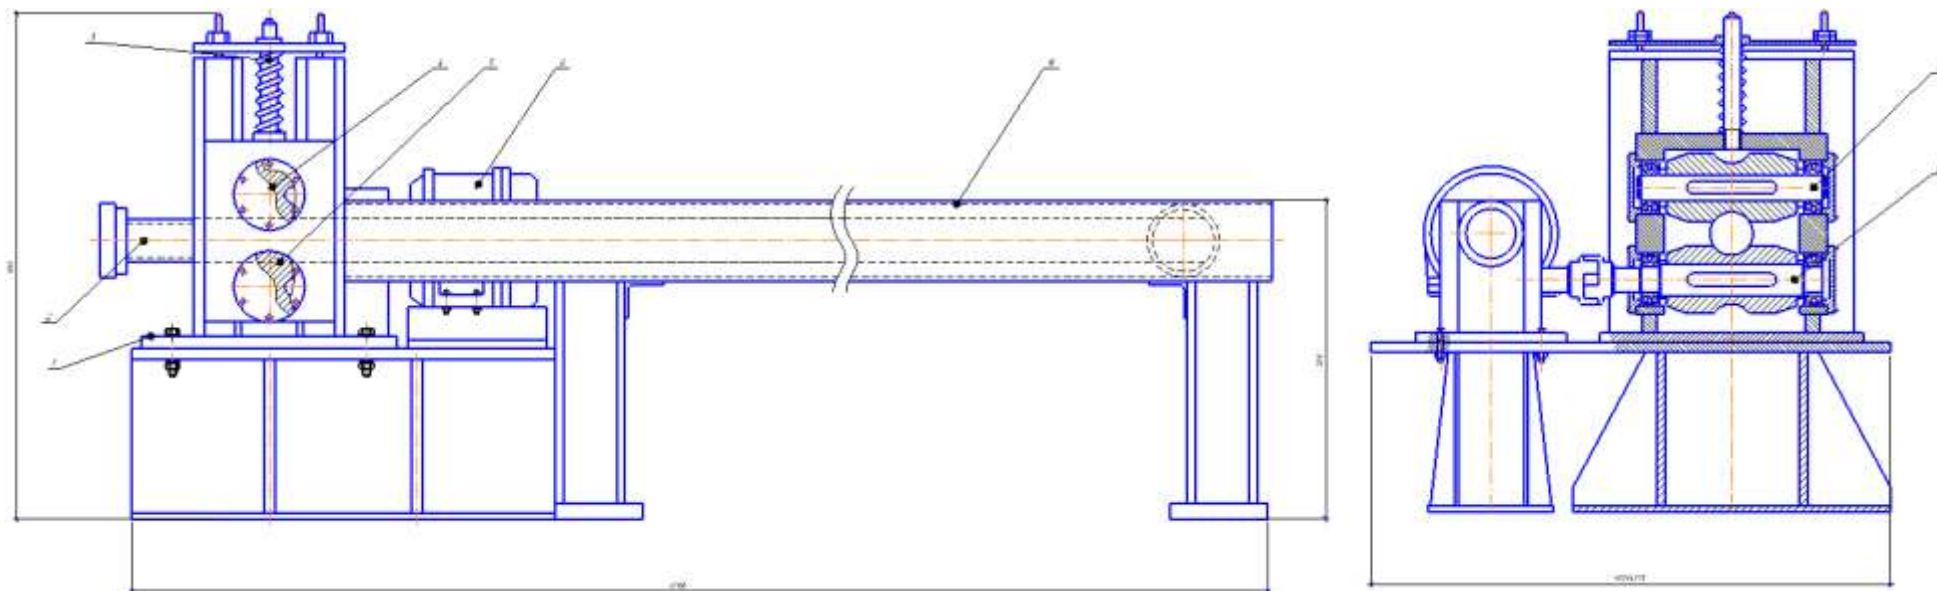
Общий вид фрикционного выталкивателя: 1 - рама; 2 - толкатель;
